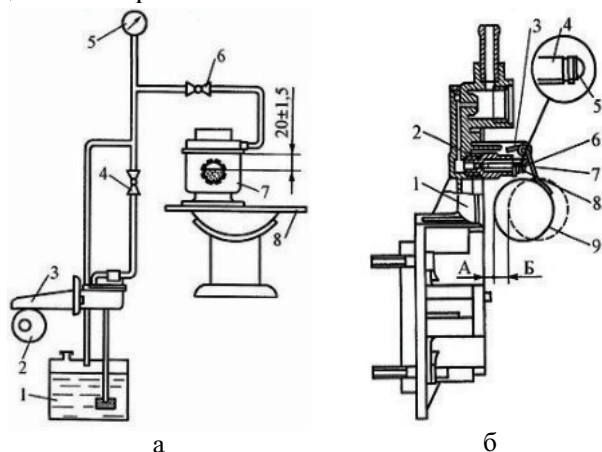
Установка для проверки и регулировки уровня топлива в поплавковой камере (а) и установка уровня топлива в поплавковой камере карбюратора типа «Озон» (б):
